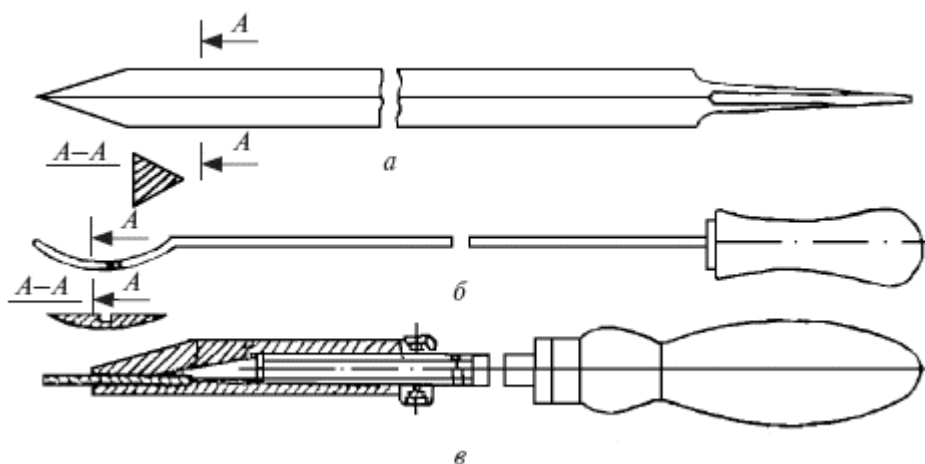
Слесарные шаберы: а – трехгранный; б – в форме ложечки; в – плоский с заменяемой пластиной из твердого сплава
